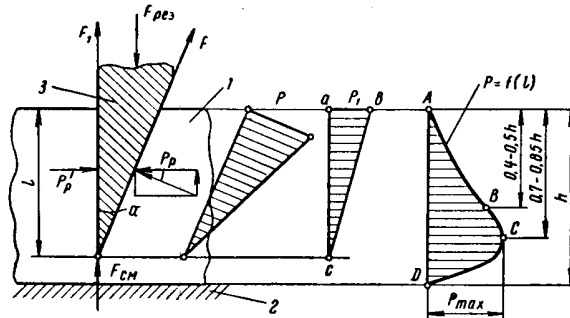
Схема вирубання деталей з листового матеріалу
